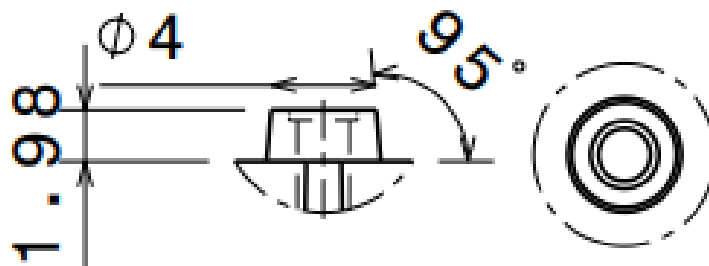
Vista em detalhe do segundo castelo do Carrier Frame e suas dimensões
